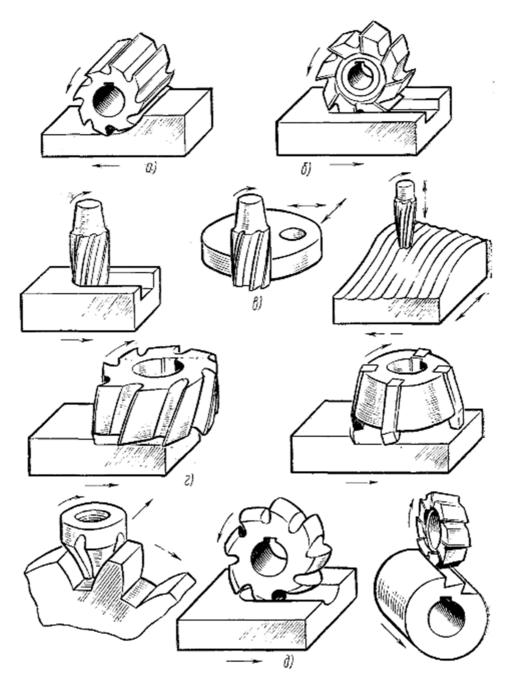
Основные типы фрез и обрабатываемых ими поверхностей
